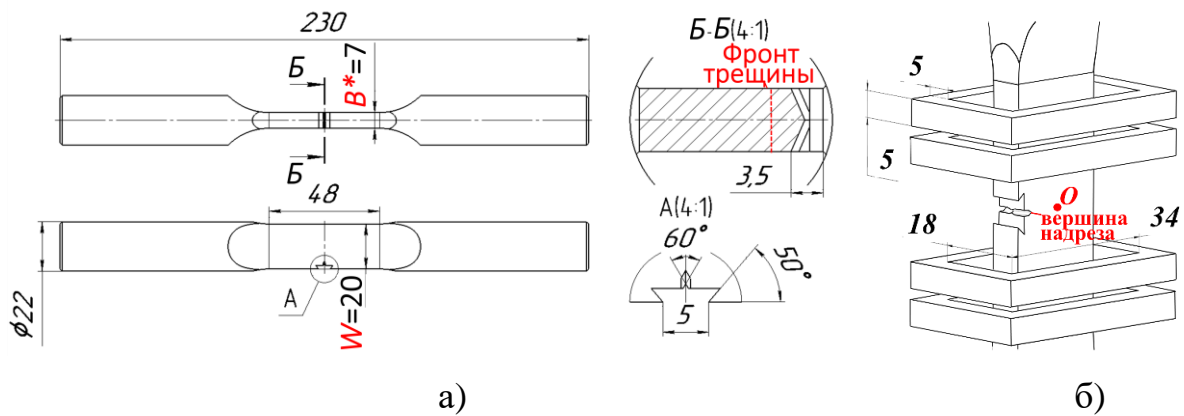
Геометрия и размеры (а) образца и (б) индуктора
